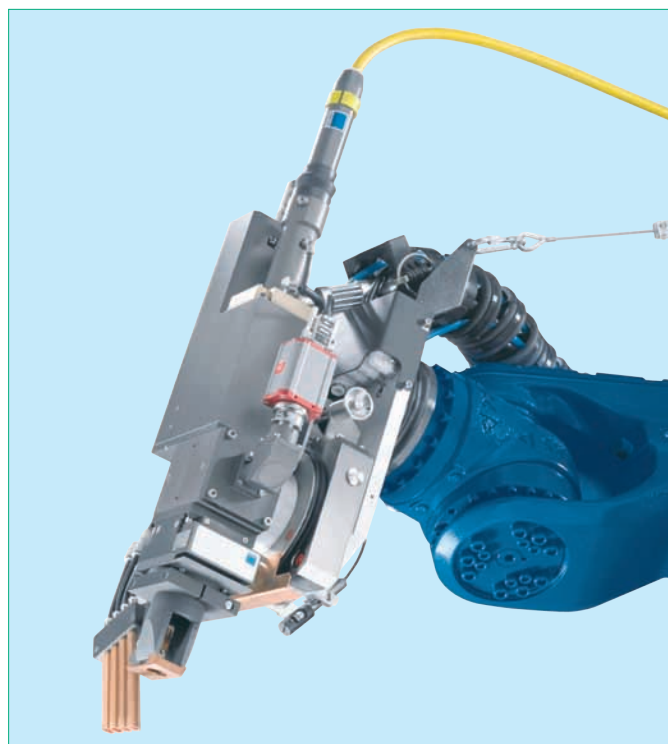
Сварочная оптика на руке робота (лазерный луч направляется к детали по гибкому световоду)
